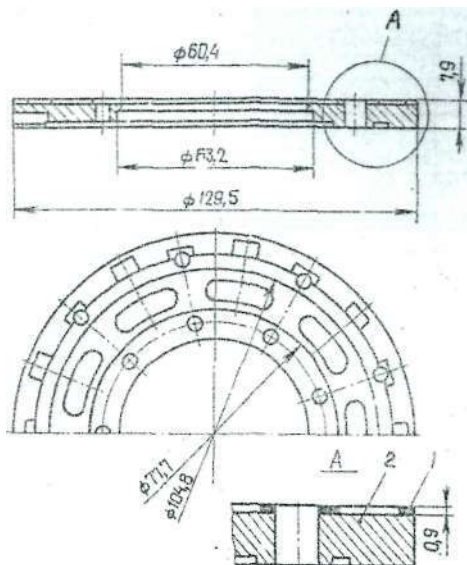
Биметаллический (сталь + бронза) подвижный распределитель объемного гидропривода: 1 - наплавленный металл; 2 - стальная основа.
